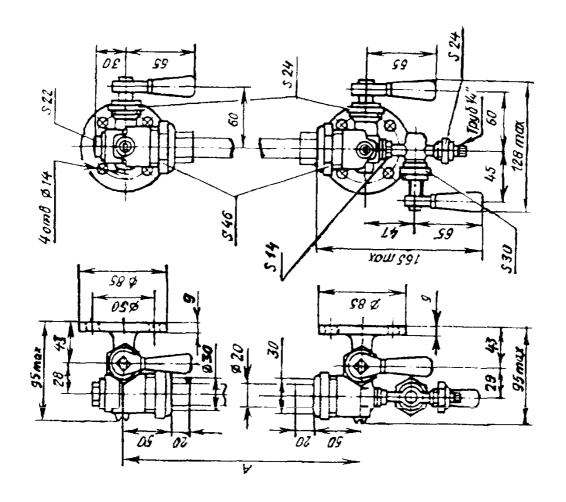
Запорные устройства типа I, исполнение Б (S - размеры под ключ)
